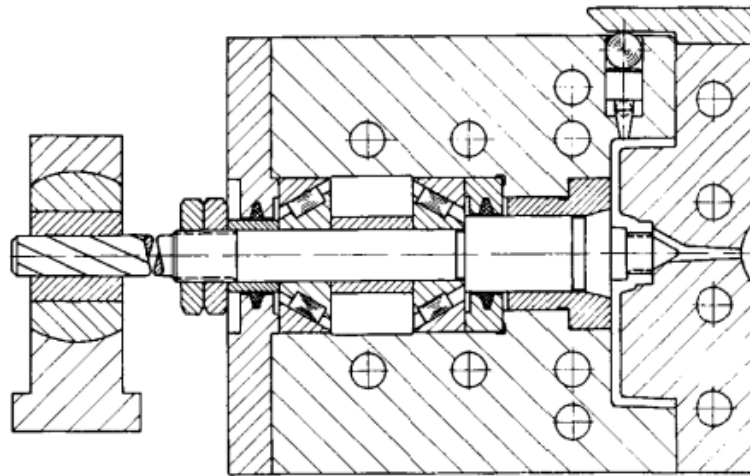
Husillo que gira en el interior del molde formando, a la vez, en núcleo de la rosca. Fuente: How to make injection molds [7].
